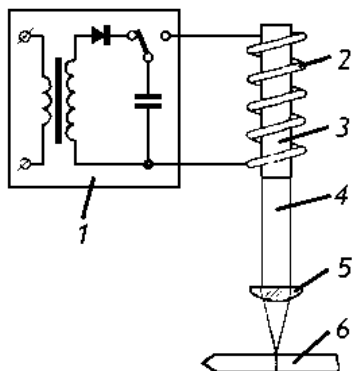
Лазерная сварка, где 1 – источник питания; 2 – лампа накачки; 3 – резонатор; 4 – луч лазера; 5 – оптическая система; 6 – свариваемое изделие
